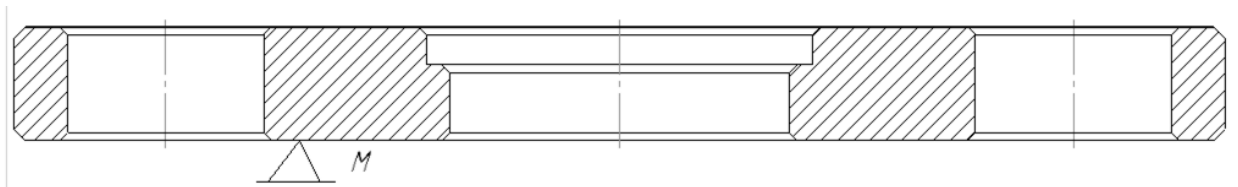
Схема базування заготовки на завершальних операціях
